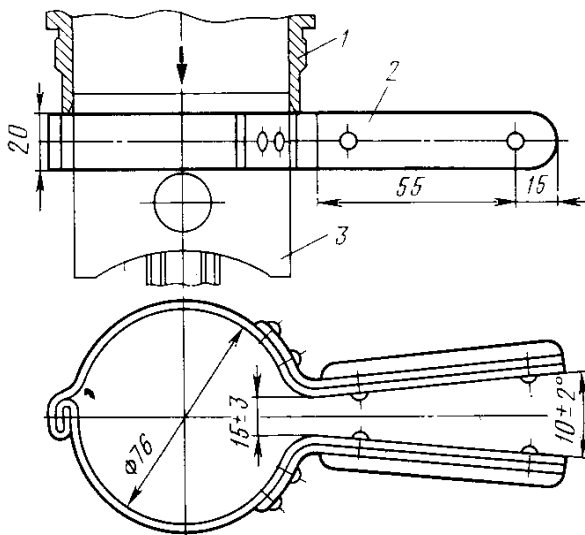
Приспособление для обжима поршневых колец: 1 — цилиндр; 2 — приспособление; 3 — поршень с кольцами
